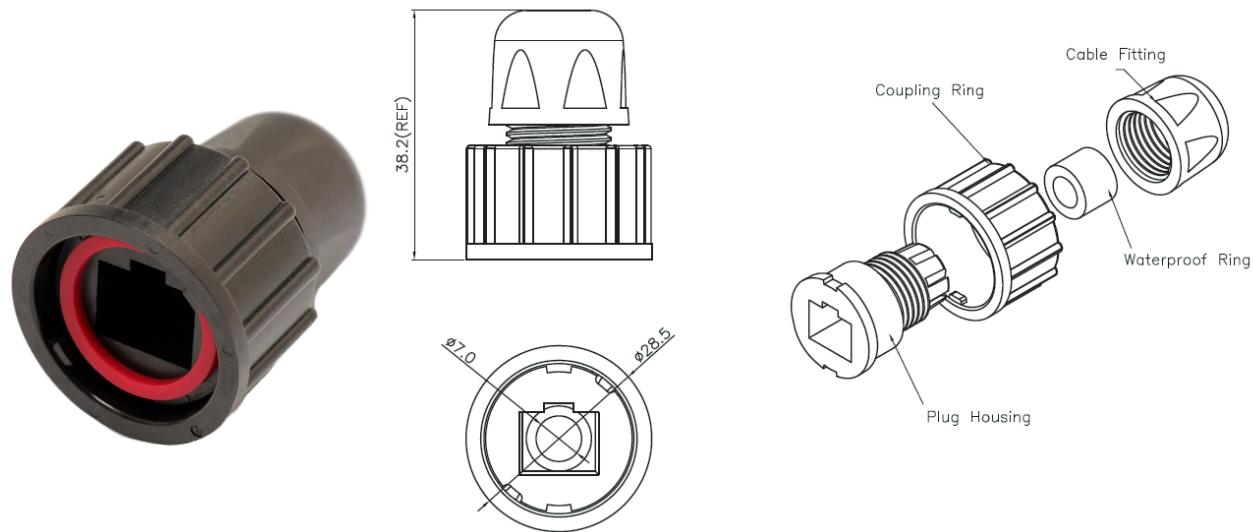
Внешний вид проходной муфты 3351L - 02 (ф. Kinsun)
